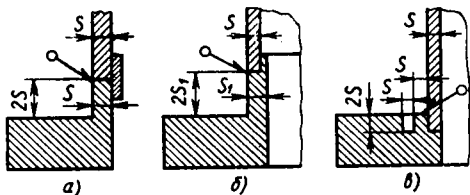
Сварка фланцев с обечайкой:
